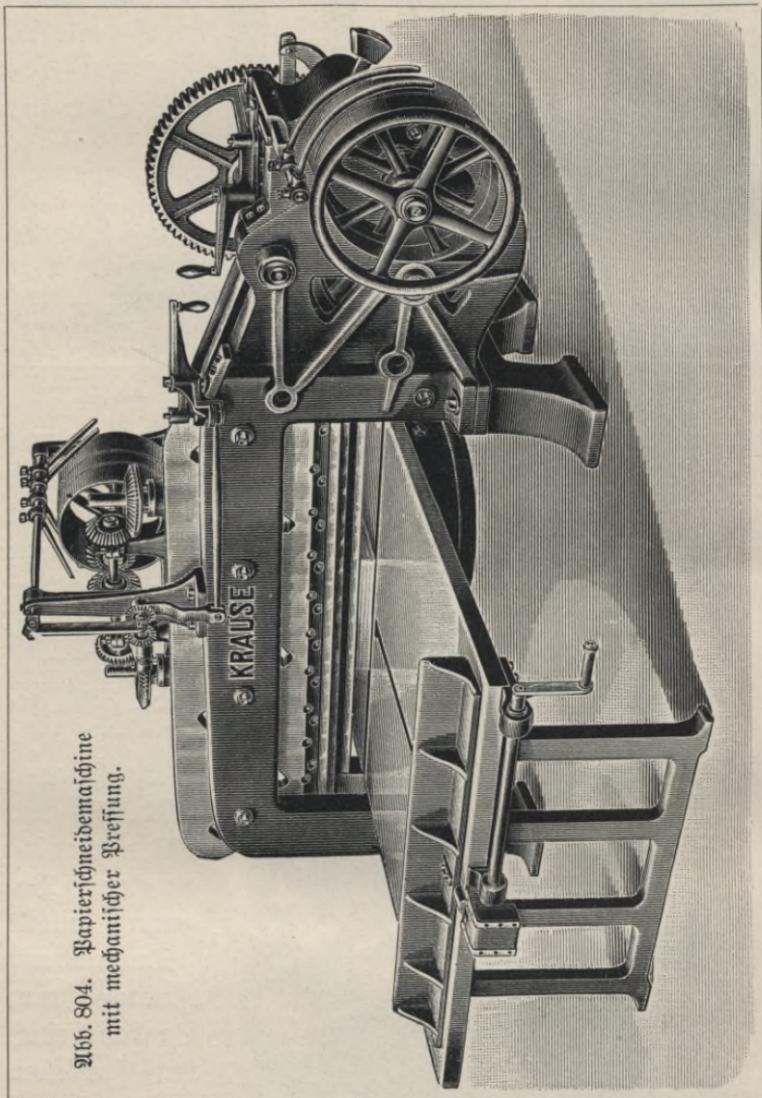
Papierschnidmaschine mit mechanischer Pressung.
